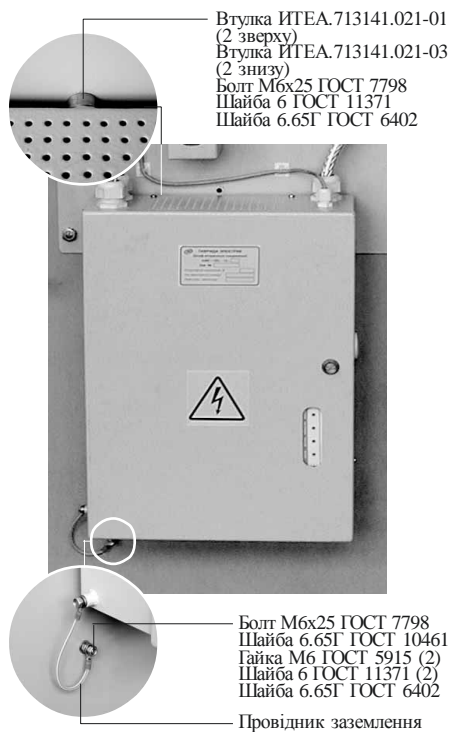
Установка і заземлення ШВС на фасаді ВЕ
